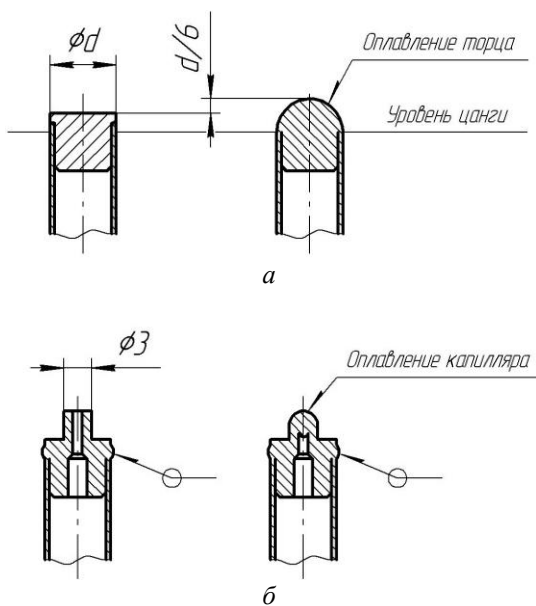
Конструкции сварных соединений, предназначенные для оплавления торца заглушки (а) и оплавления торца капилляра, приваренного к оболочке (б), до и после герметизации
